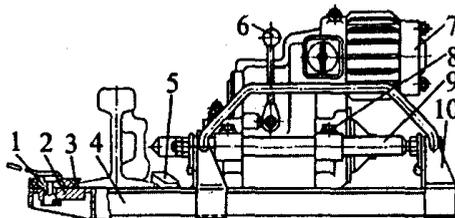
Рельсоверлильный станок РСМ- 1
